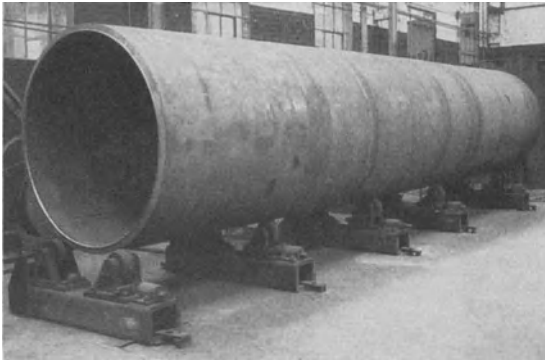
Geschweißter Mantel eines Hochdruckkessels auf Rollenböcken.
